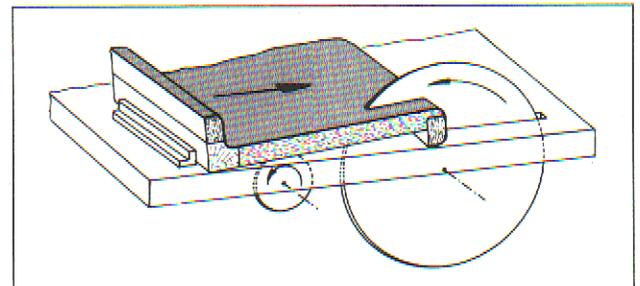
Fertigschnitt an einem Z-förmigen Verbundelement mit Hauptsägeblatt großen Durchmessers und Ritzsäge.
